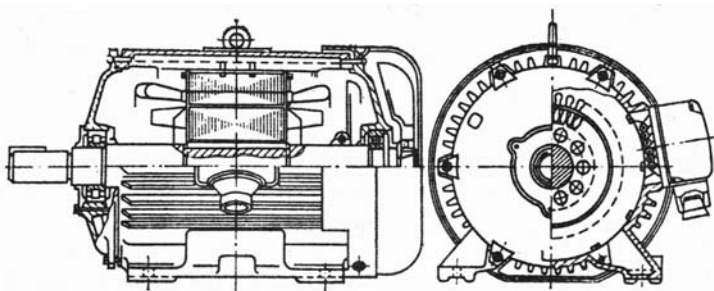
Обдуваемый асинхронный двигатель АО 9-го габарита
